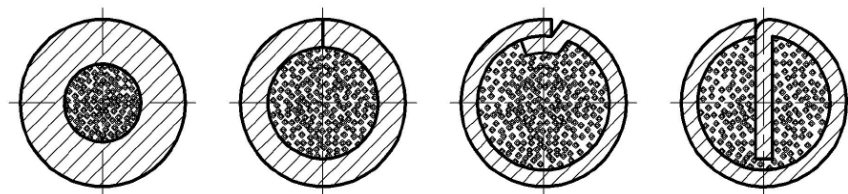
Некоторые конструкции сварочной порошковой проволоки [1]
